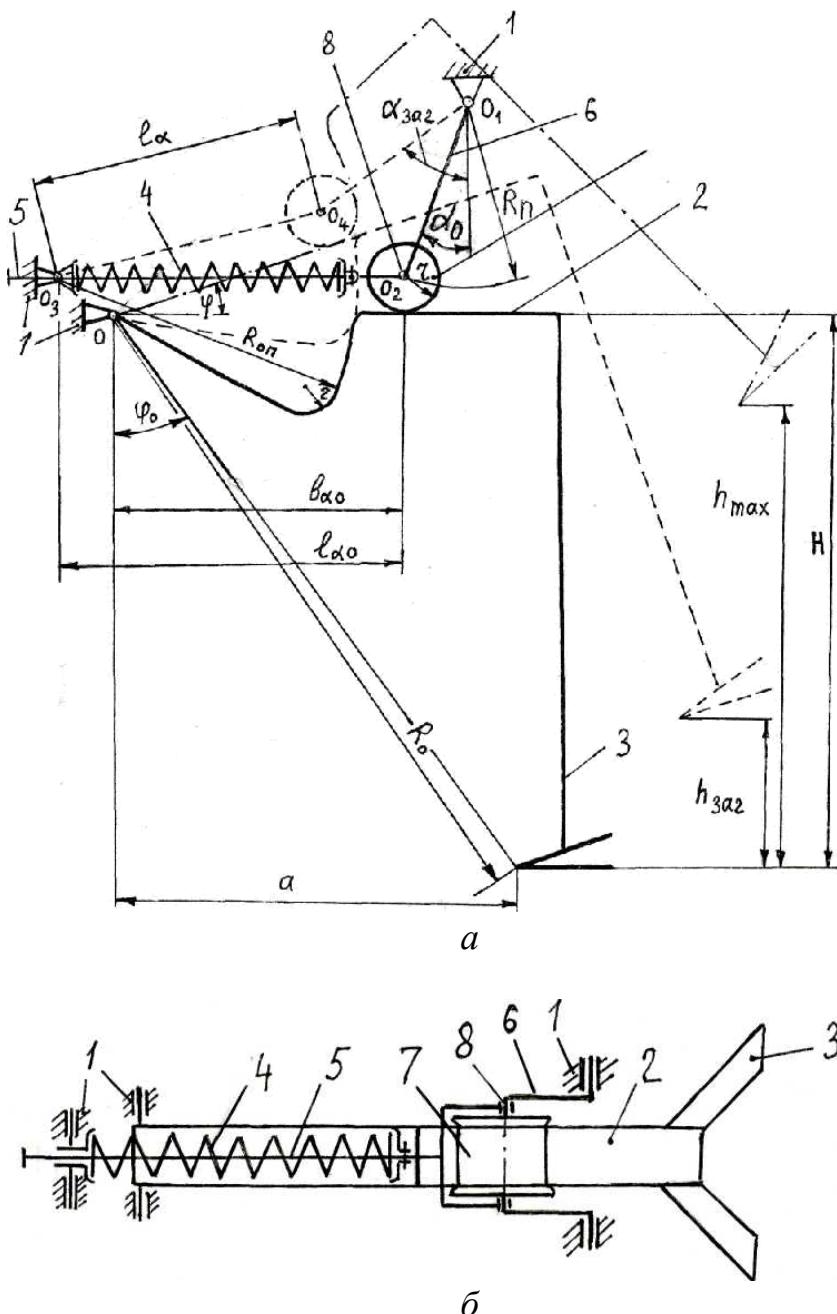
Глубокорыхлитель: 1 – рама; 2 – грядиль; 3 – рабочий орган; 4 – пружина сжатия; 5 – нажимная штанга; 6 – поводок; 7 – ролик; 8 – ось;
